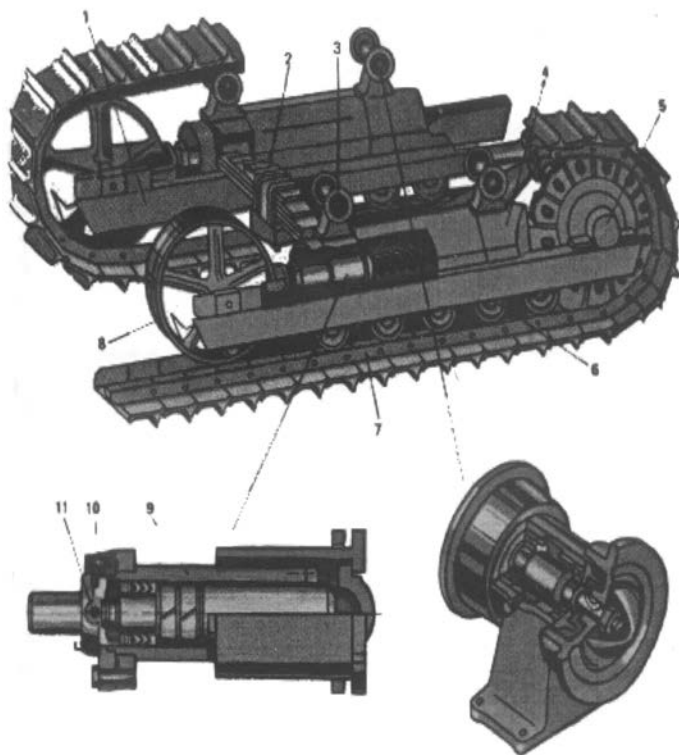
Ходовая часть гусеничного трактора: 1 – рама гусеничной тележки, 2 – рессора, 3 – поддерживающий каток, 4 – гусеничная тележка, 5 – подшипник опоры ведущего колеса, 6 – опорный каток, 7 – гусеницы, 8 – направляющие колеса, 9 – натяжное устройство, 10 – пробка, 11 – масленка
